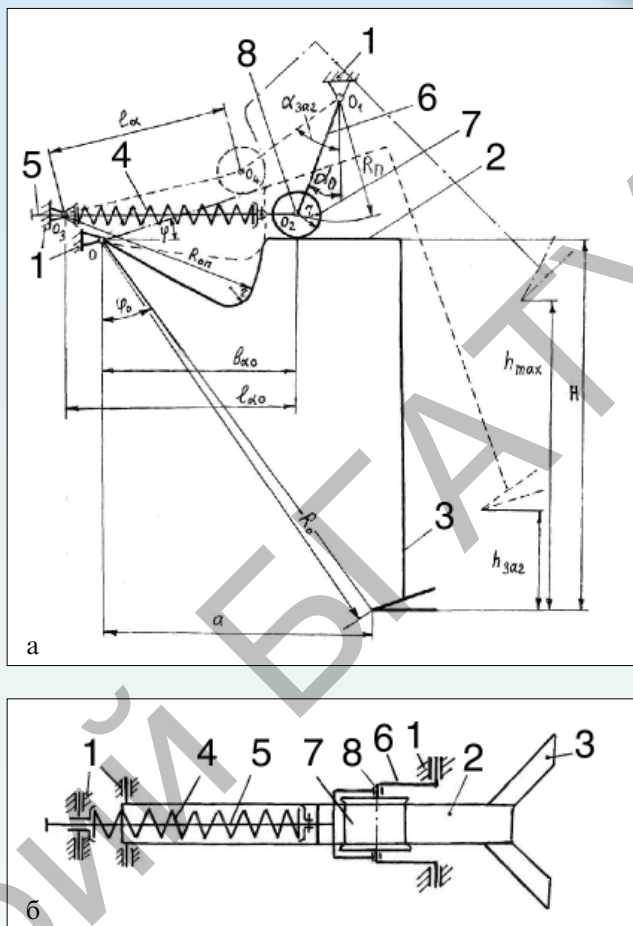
Глубокорыхлитель: а – вид сбоку; б – вид сверху
